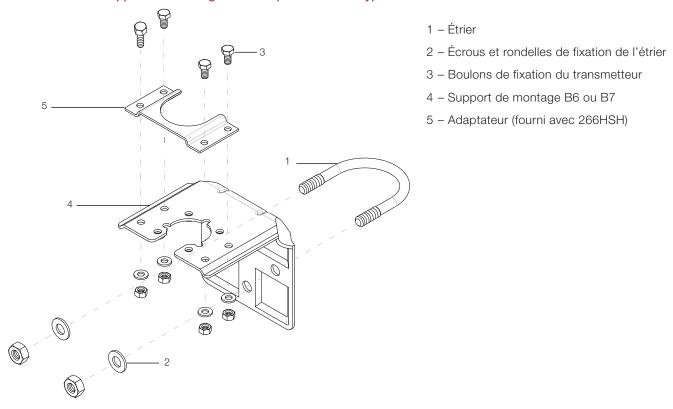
Support de montage mural ou sur tuyau pour transmetteur de type P avec boîtier type barillet
